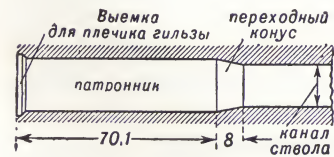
Профиль патронника и канала ствола охотничьего ружья.
